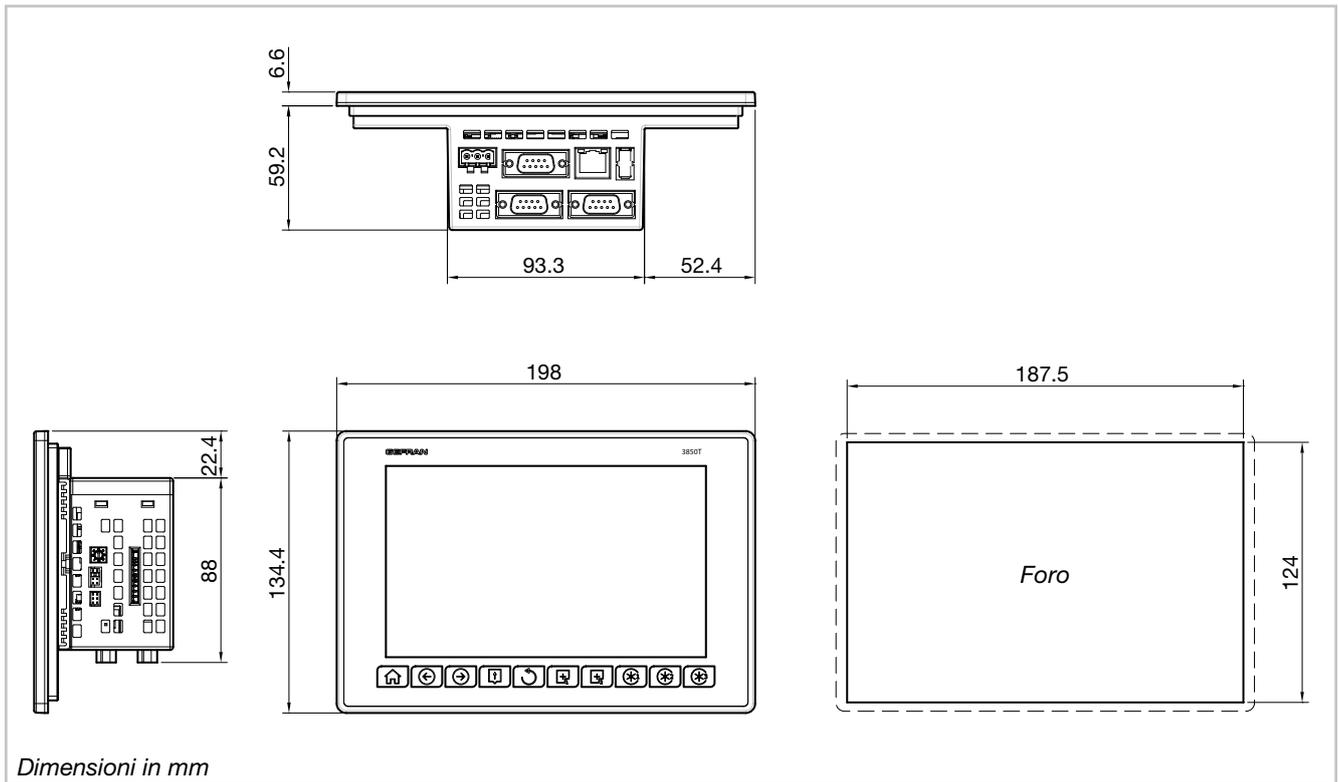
Dimensioni e dime di foratura interfaccia 3850T
